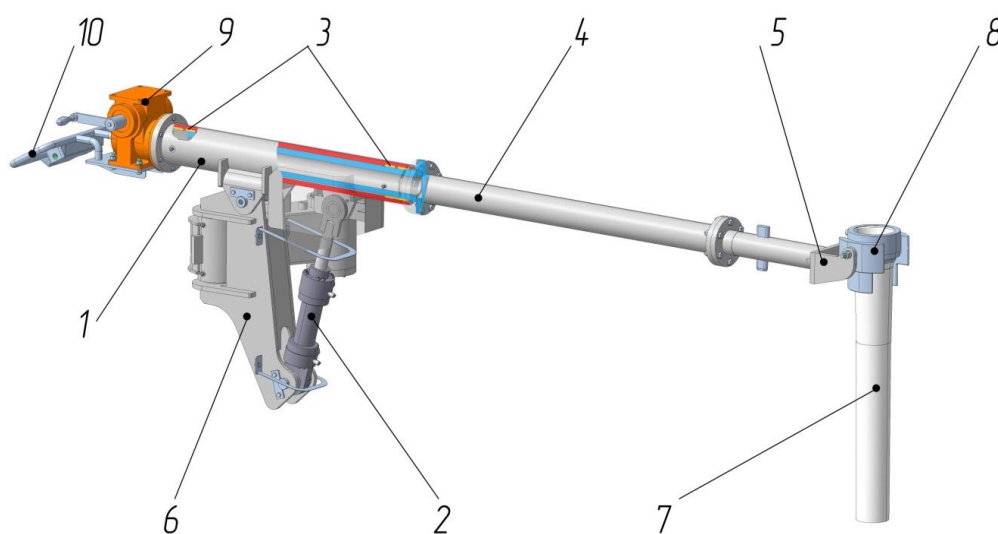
Стріла: 1 – гільза; 2 – гідроциліндр; 3 – підшипники ковзання; 4 – збірна консоль; 5 – кутник; 6 – кронштейн; 7 – обертальний захват; 8 – кошик; 9 – редуктор; 10 – керуючий пристрій
